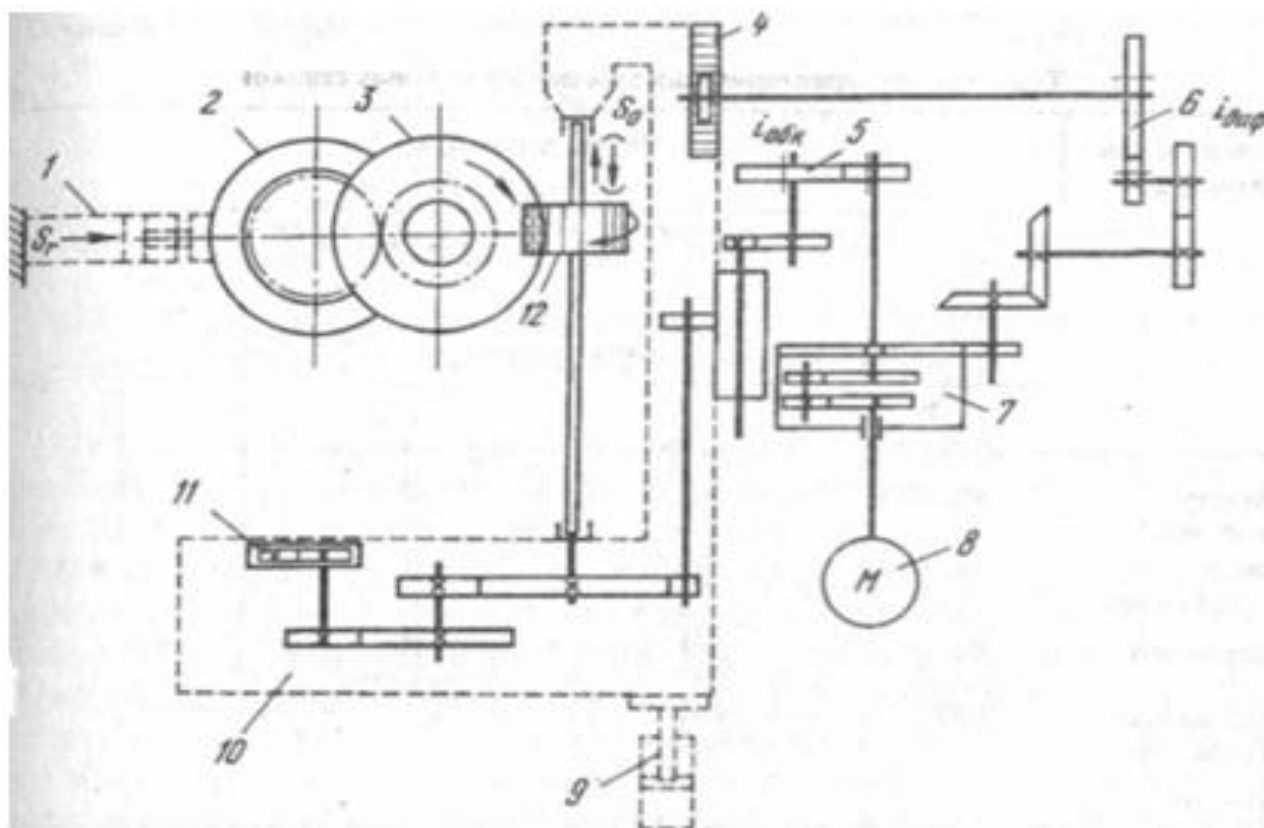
Кинематическая схема зубошлифовального станка, работающего червячным абразивом (непрерывная схема шлифования): 1 - гидравлический привод каретки шлифовального круга. 2 – синхронный двигатель привода инструмента, 3 – абразивный червяк. 4 – зубчато-реечная передача, 5 - делительная гитара цепи обката, 6 – гитара дифференциала. 7 – дифференциал, 8 - синхронный двигатель привода детали, 9 – гидравлический привод каретки изделия, 10 – каретка изделия, 11 – гидравлический тормоз, 12 – заготовка.
